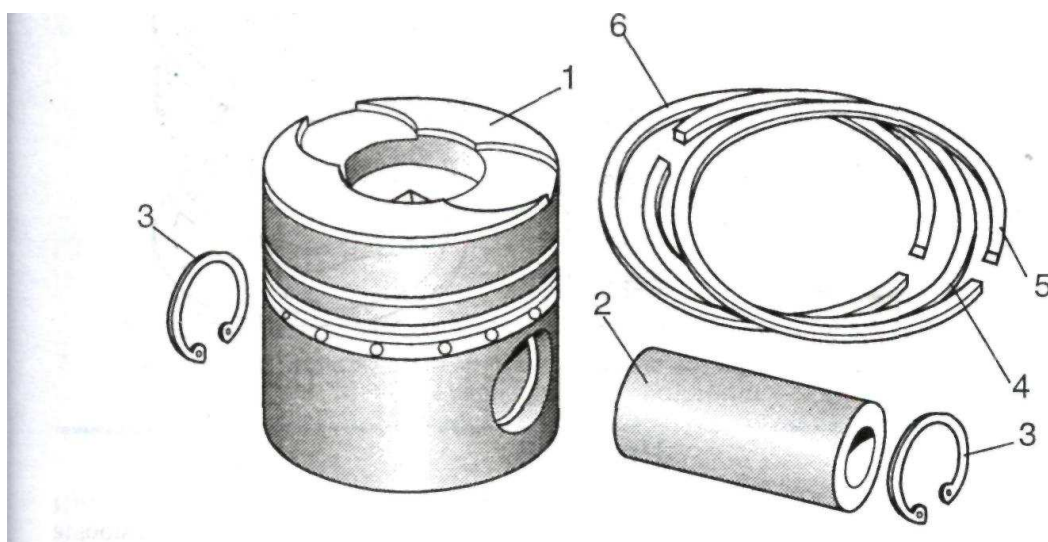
Деталі поршневої групи дизеля КамАЗ-740:
